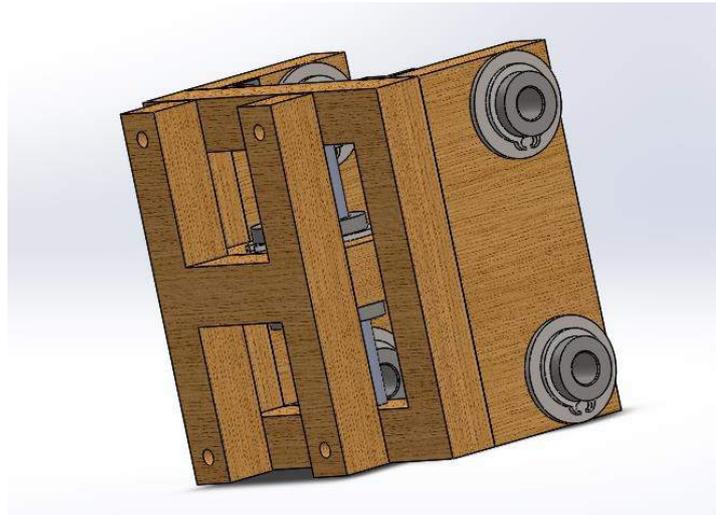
Acoplamento da ferramenta. Desenho em SolidWorks.
